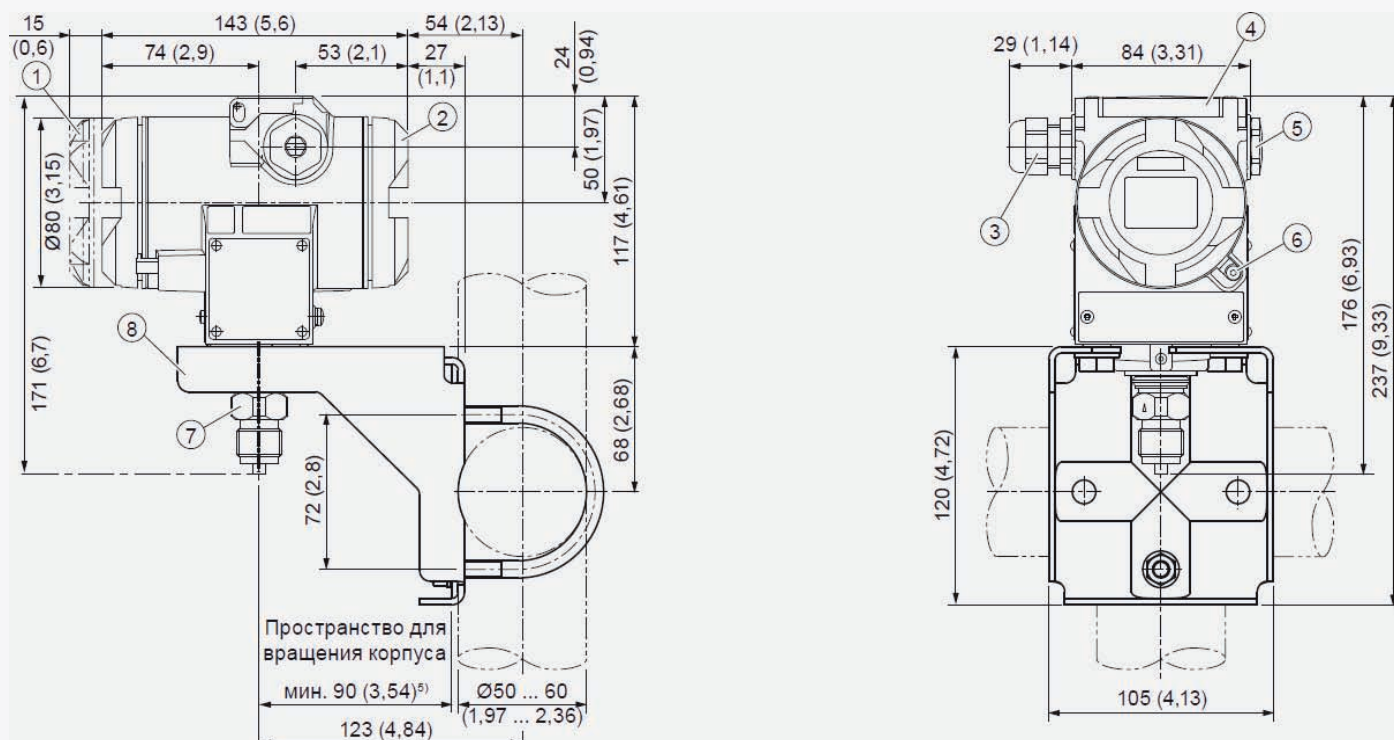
Измерительный преобразователь КМ35 в корпусе избыточного давления, размеры в мм (дюймах)
